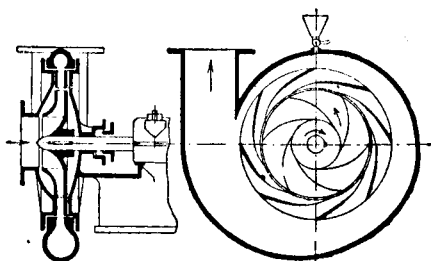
Одноколесный центробежный насос с направляющим аппаратом.
